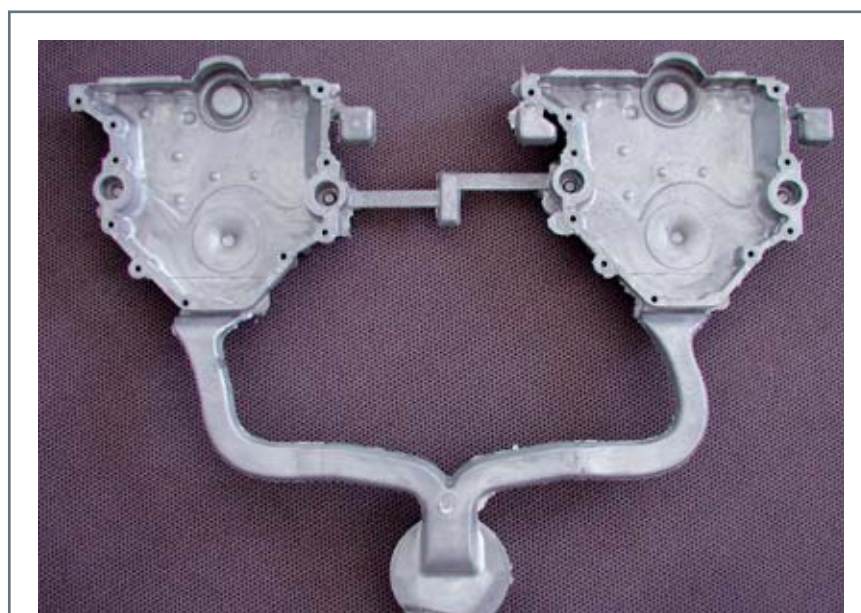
Realisierung des optimierten Gießlaufes für das Zweifachwerkzeug – die im Rechenmodell ermittelten Gießläufe wurden in das Werkzeug übertragen.
